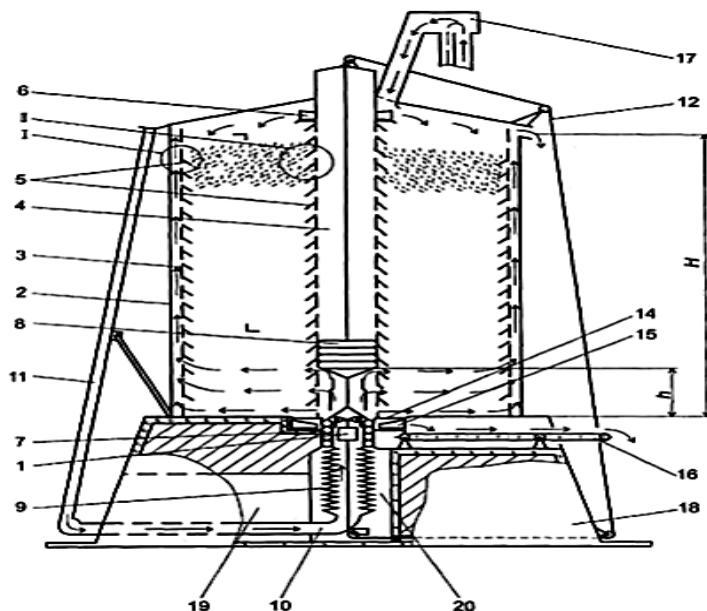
Загальний вигляд зерносховища-сушарки
